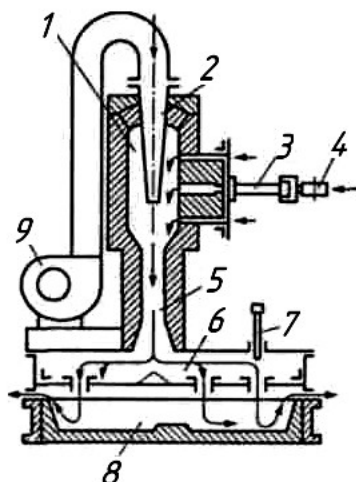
Переносное газовое сушило: 1 – топка; 2 – сопло; 3 – горелка; 4 – гибкий шланг; 5 – газовый смеситель; 6 – распределительная камера; 7 – термометр; 8 – форма; 9 – вентилятор
